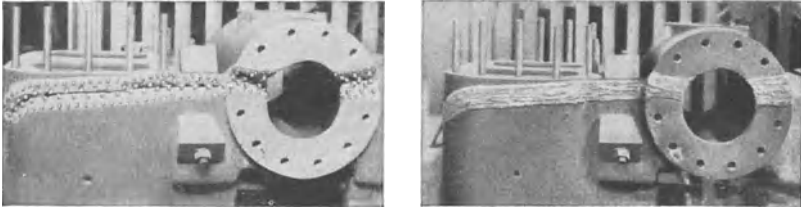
u. 317. Kaltschweißung eines Gußzylinders.
